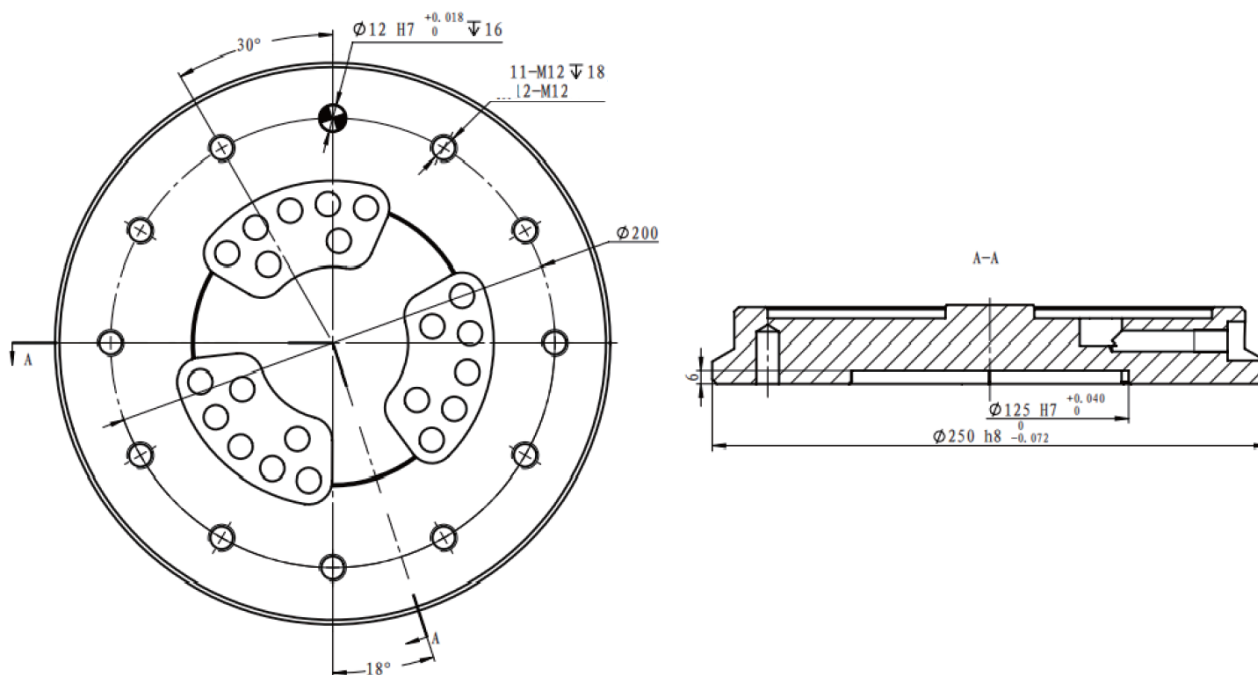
Габаритные чертежи робота-манипулятора SR280-2850.
